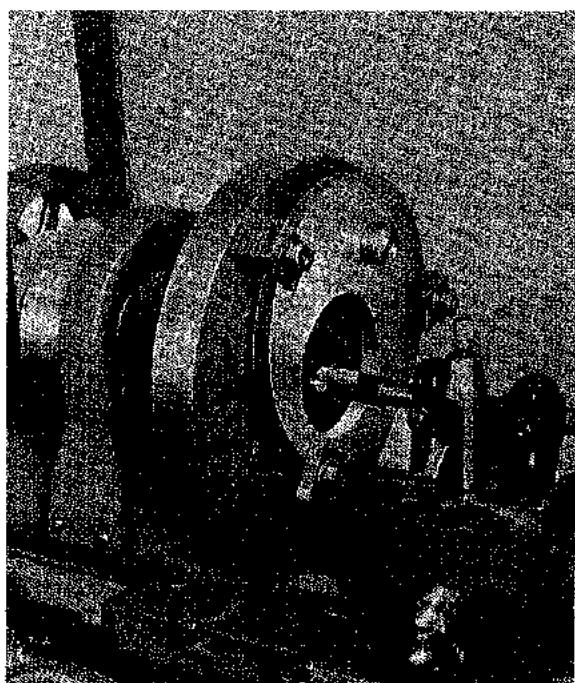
Disposición para el mandrinado de un agujero (South Bend Lathe Works).
